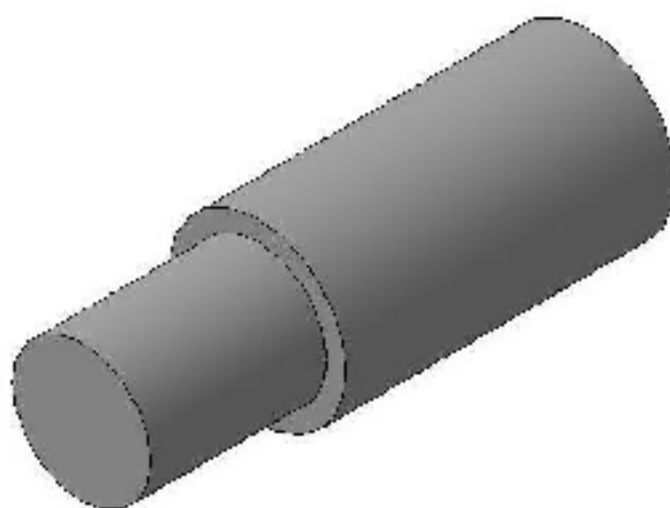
3D-модель поковки при штампуванні на КГШП
